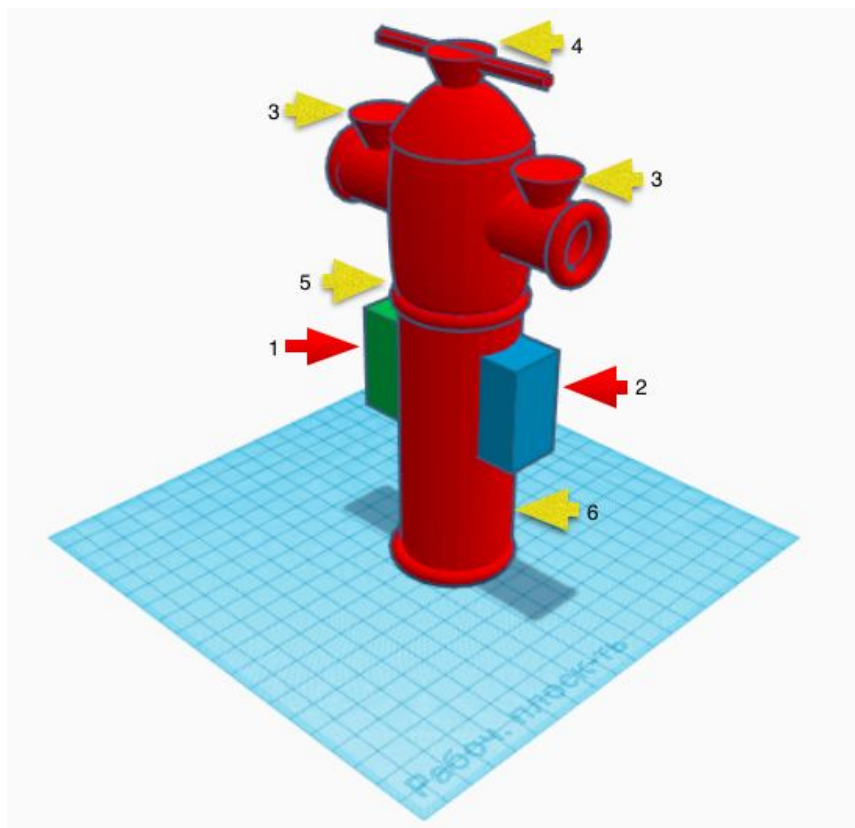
Колонка пожарная разборная. 1–расходомер; 2–манометр; 3–маховик вентиля; 4–торцевой ключ; 5–верхний корпус; 6–нижний корпус
